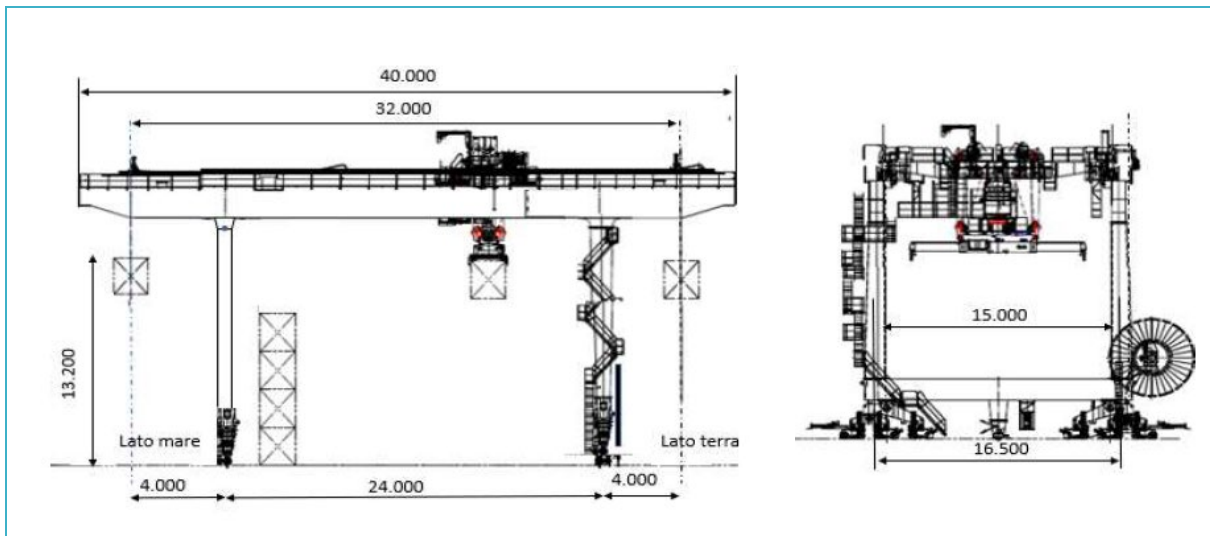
Sezione tipologica (a destra ortogonale rispetto alla banchina, a sinistra parallela rispetto alla banchina) della gru a cavalletto
